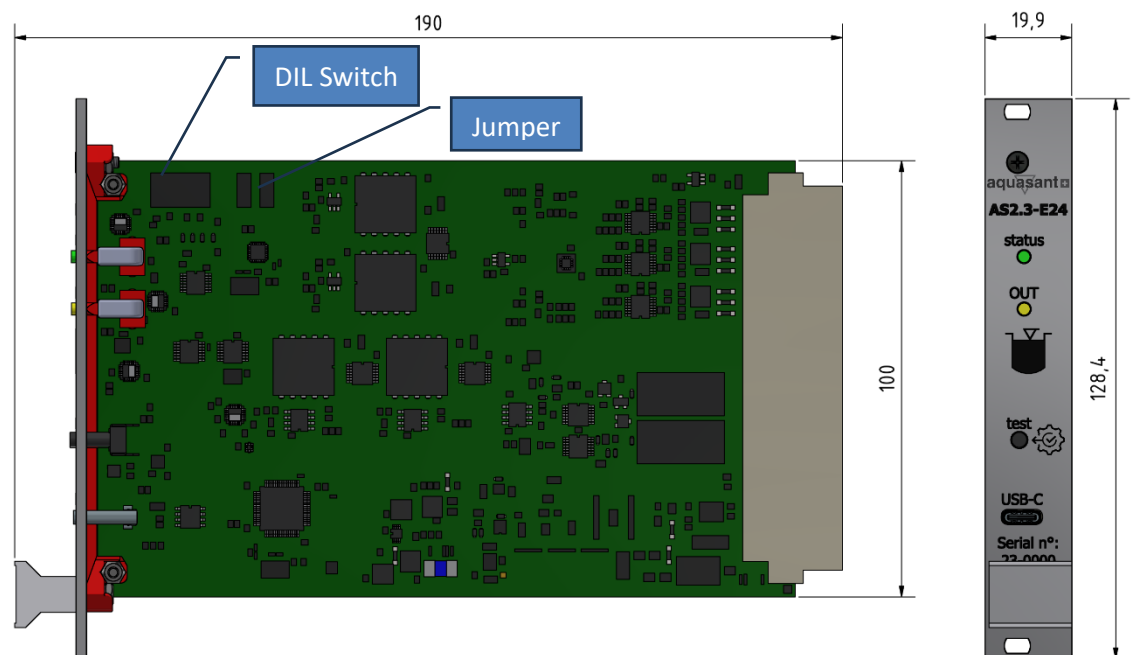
Gerätedimensionen, Auf-, Seitenansicht
